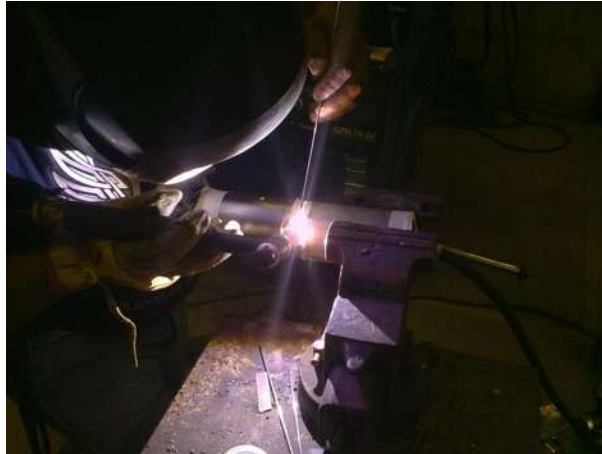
Aplicación del proceso de soldadura.
